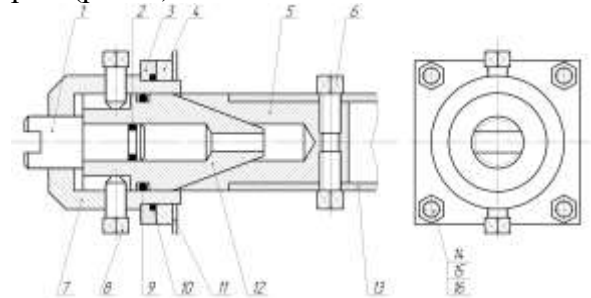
Конічний підшипник ковзання, що регулюється: 1 – гвинт притискний; 2 – кільце ущільнюоче; 3, 4 – фланець; 5 – вставка; 6 – гвинт; 7 – корпус; 8 – гвинт; 9, 10 – ущільнення гумове; 11 – корпус; 12 – цапфа; 13 – вал; 14 – шпилька; 15 – гайка; 16 – шайба
